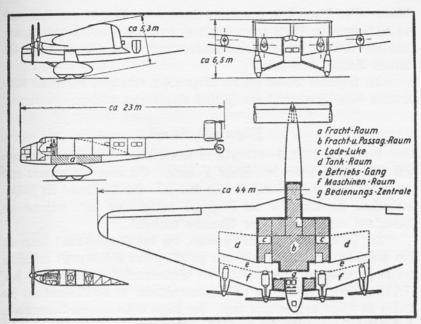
Junters-Großslugzeug G 38, Abersichtsstizze.
